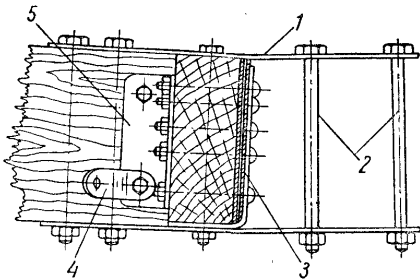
Задний узел крепления нижнего крыла. 1—верхняя пластина; 2—болты для крепления крыла к фюзеляжу; 3—обойма; 4—ушко для крепления нижней ленты-расчалки; 5—угольник.
